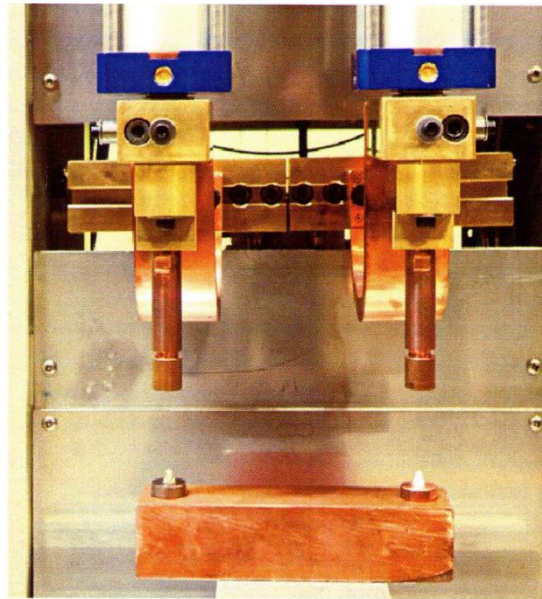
Pormenor da máquina de soldadura em estudo
